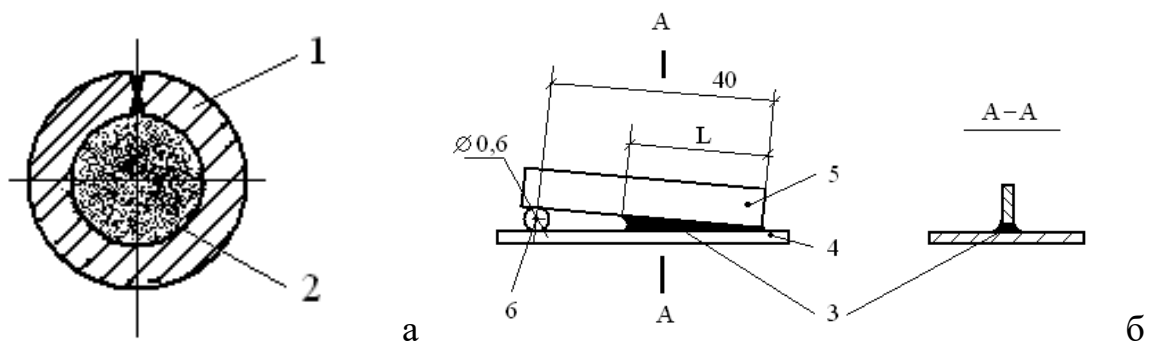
Поперечний перетин порошкового дроту (а): 1 – трубчаста оболонка з алюмінієвого припою; 2 – реактивний флюс-наповнювач; зовнішній вид паяного зразка (б): 3 – припій, 4 – верхня пластина розміром 45x5x1 мм, 5 – нижня пластина розміром 40x30x1 мм, 6 – упор-циліндр діаметром 0,6 мм довжиною 10 мм.
